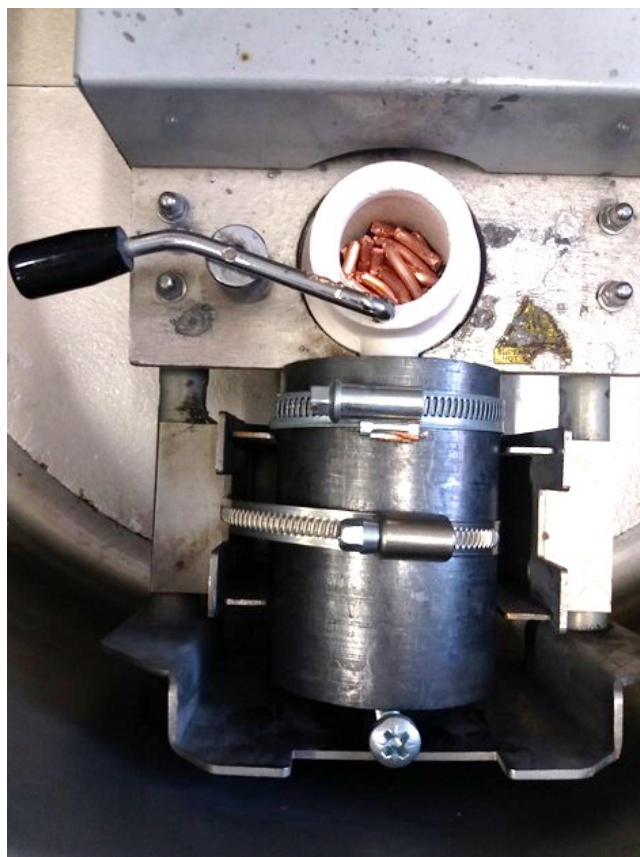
Kabelová Cu drť pro 8 tavbu
